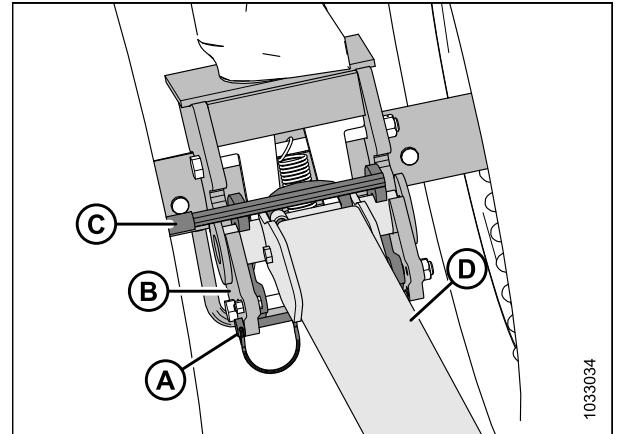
Удлинитель буксирной тяги и транспортный шарнир
